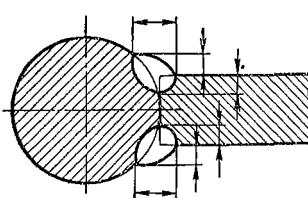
Указание конструктивных элементов нестандартного шва сварного соединения
